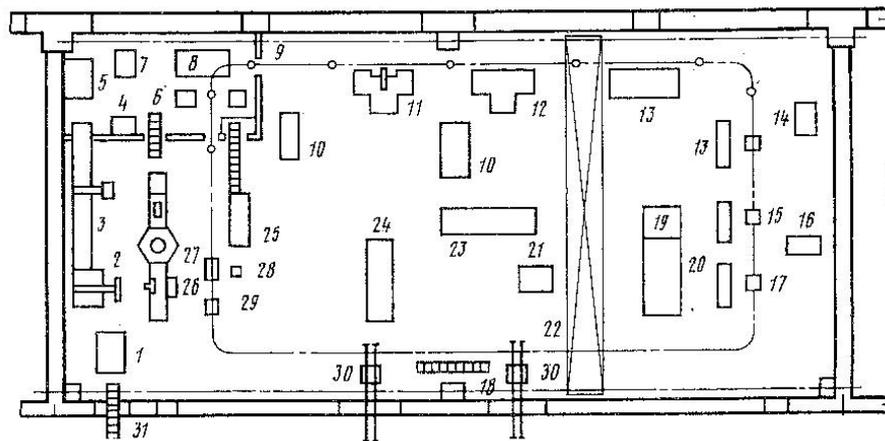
План контрольного пункта автосцепки: 1 – контейнеры для поглощающих аппаратов; 2 – стол для осмотра и определения объема ремонта тяговых хомутов; 3 – поточная линия для ремонта тяговых хомутов; 4 – стенд для наплавки тяговых хомутов; 5 – сварочный стол; 6 – рольганг; 7 – полуавтомат А-765; 8 – стенд-кантователь для наплавки автосцепки; 9 – подвесной монорельс; 10 – стеллаж-верстак; 11 – вертикально-фрезерный станок; 12 – горизонтально-фрезерный станок; 13 – верстак; 14 – наждачно-шлифовальный станок с гибким валом; 15 – стенд для обработки шина автосцепки; 16 – стеллаж; 17 – сборочный стенд; 18 – кассета обоим для автосцепки; 19 – стенд для клеймения деталей; 20 – стеллаж для отремонтированных деталей автосцепки; 21 – контейнер для деталей автосцепки; 22 – кран-балка грузоподъемностью 0,5 т; 23 – слесарный верстак; 24 – шкаф для инструмента и шаблонов; 25 – стол для проверки деталей автосцепки; 26 – кассета упорных плит; 27 – стенд для ремонта поглощающих аппаратов; 28 – стенд для разборки механизма сцепления автосцепки; 29 – установка для дефектоскопии хвостовика автосцепки; 30 – механизированная тележка для транспортировки автосцепок; 31 – рольганг для подачи комплектов поглощающих аппаратов.
